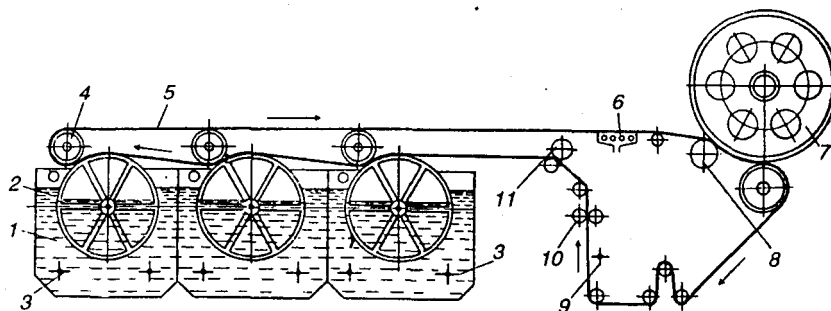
Схема работы листоформовочной трехцилиндровой машины: 1 — ванна; 2 — полные барабаны с сетчатой поверхностью; 3 — асбестоцементная масса; 4 — прижимной валик; 5 — бесконечная лента сукна; 6 — вакуумная коробка; 7 — форматный барабан; 8 — опорный вал; 9 — пресс-вал; 10 — промывное устройство; 11 — отжимные валики
